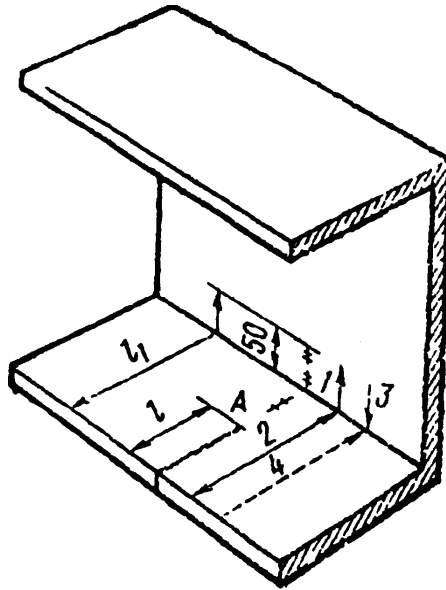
Ескіз підготовки і зварювання тріщин моторної балки
